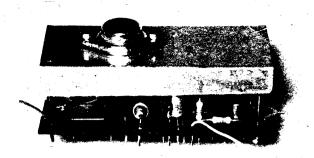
Možnost uchycení chladicí desky měděným drátem o Ø 1 mm
